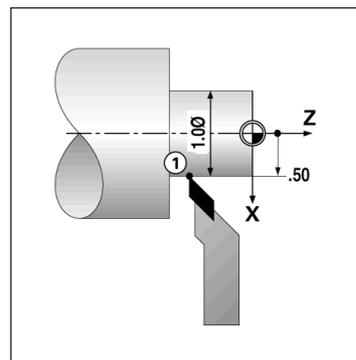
Werkstück zum Beispiel „Durchmesser- und Radius-Anzeige“
